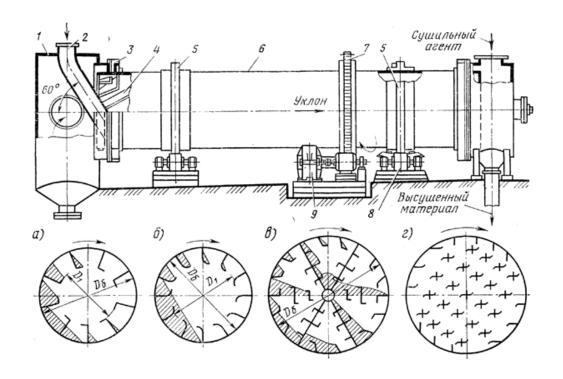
Барабанная сушильная установка: 1 — камера для отвода сушильного агента; 2 — подача сырого материала; 3 — уплотнительное кольцо; 4 — насадка; 5 — скользящая опора; 6 — барабан; 7 — колесо привода; 8 — опорно-упорный подшипник; 9 — электродвигатель с редуктором; а и б — подъемно-лопастная система насадки; в — распределительно-перевалочная система с закрытыми ячейками; г — распределительная система.
